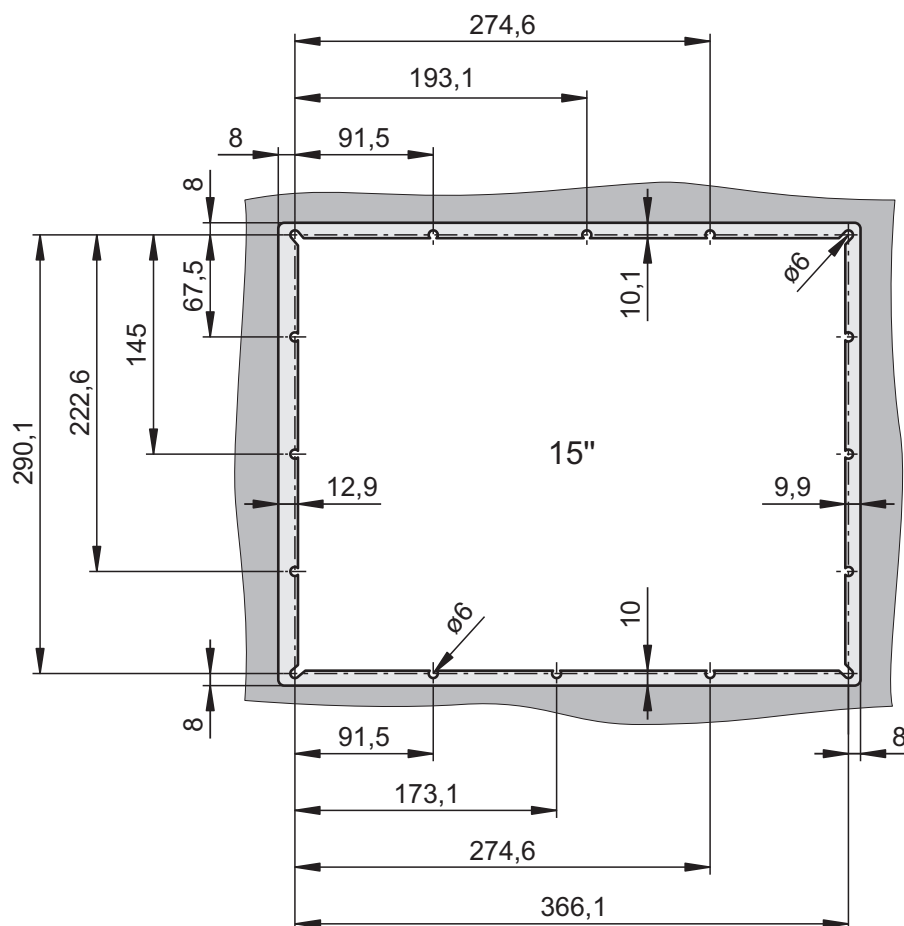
Plan de perçage écran tactile 15 " (vue de face de l'appareil, toutes les dimensions en mm)
